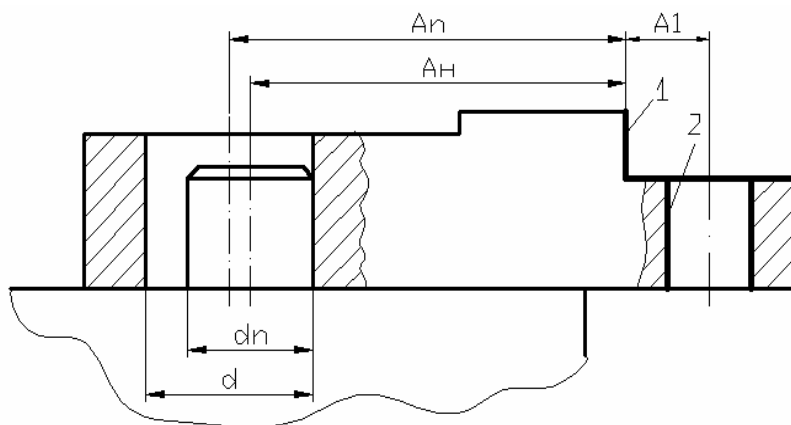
Установка заготовки по отверстию на цилиндрический палец
